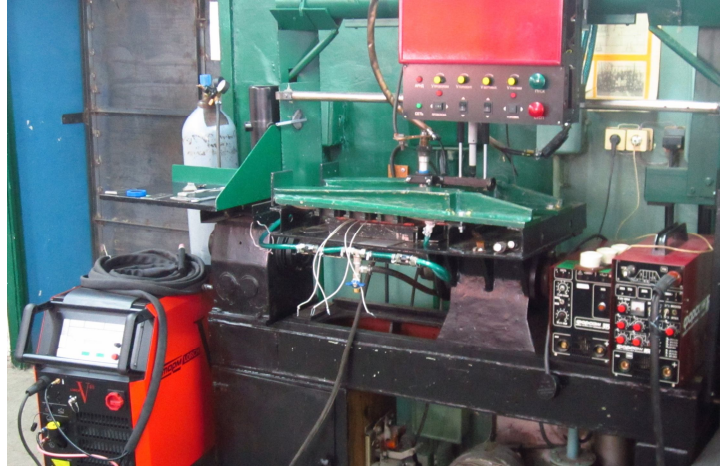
Стенд для сварки плоских образцов
